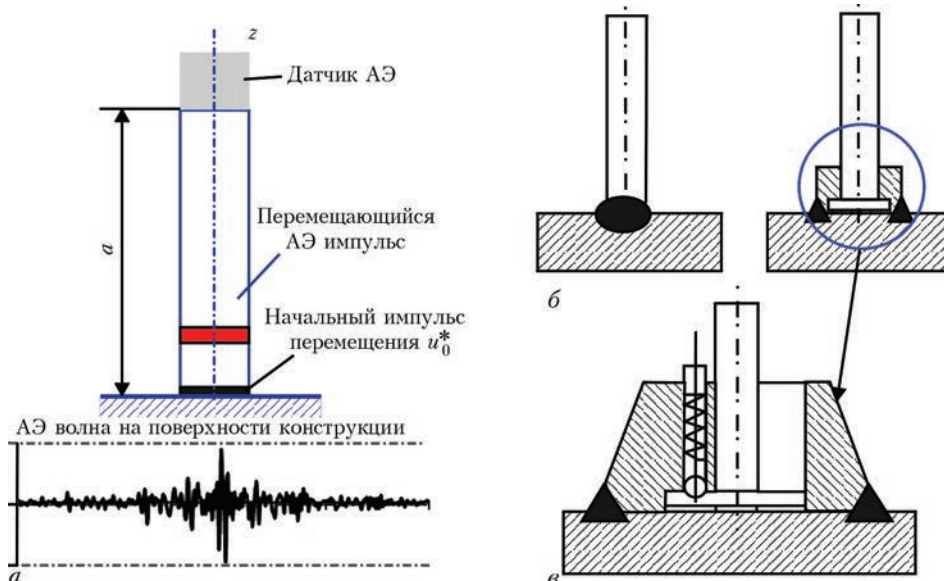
Схема конструкции волновода (а) и способы его крепления к поверхности контролируемой конструкции (б), конструкция баяннетного замка для крепления волновода к поверхности изделия (в)
